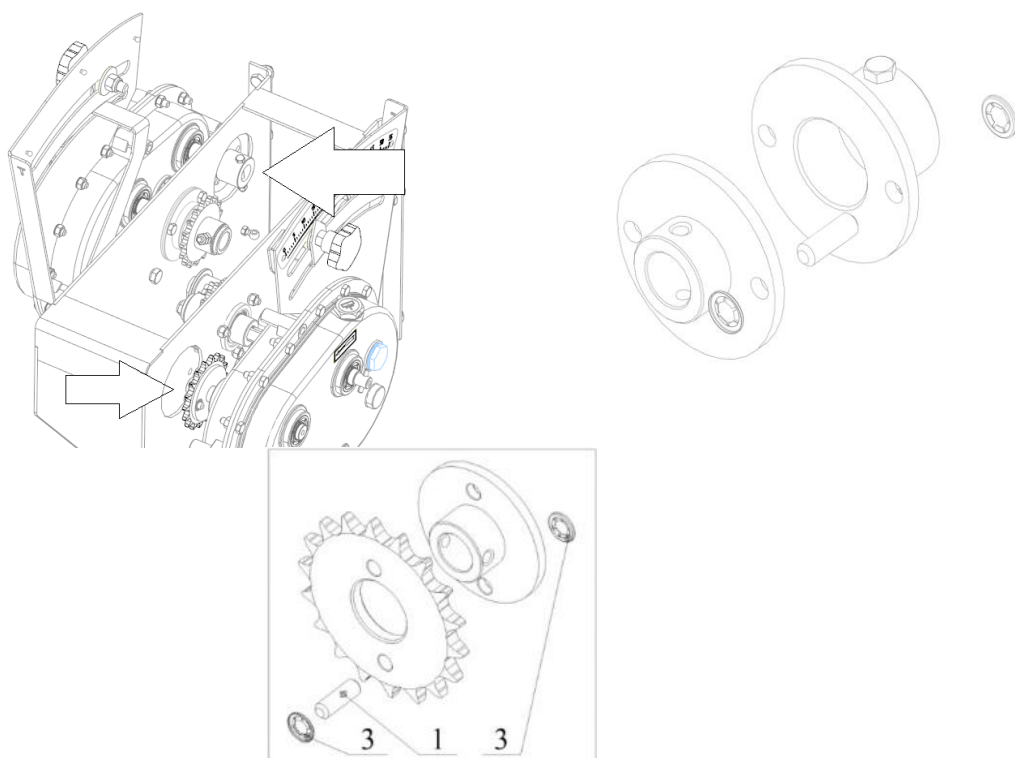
Размещение и устройство предохранительных муфт. 1- предохранительный полимерный штифт. 3 – шайба starlock
